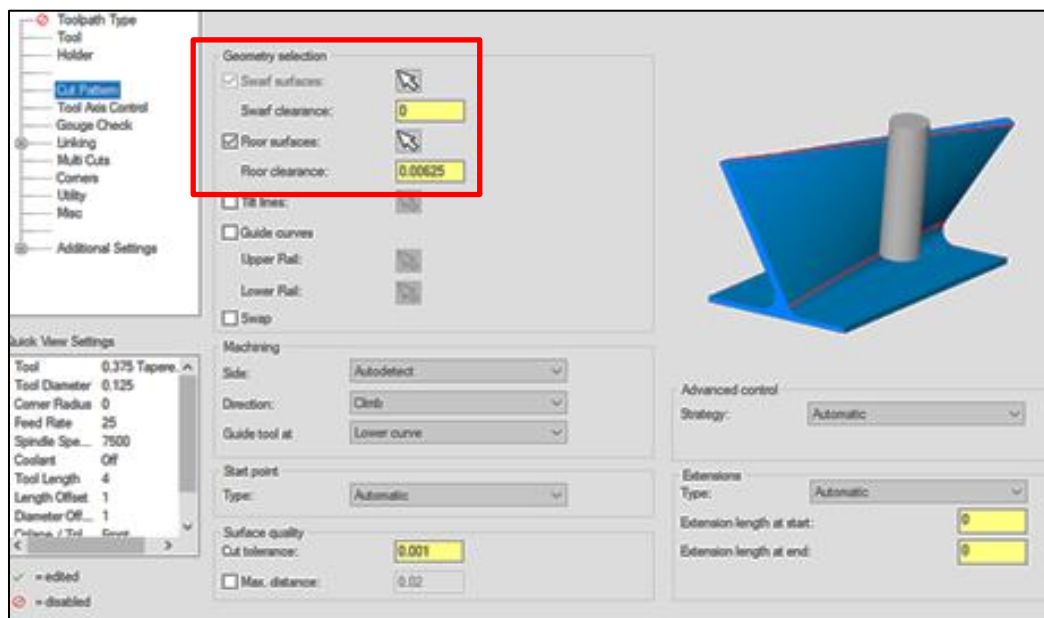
Definiendo patrón de corte para el acabado de la pieza [fuente propia]
